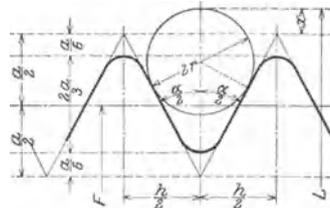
Gewindemessung mittels kalibrierter Drähte.
